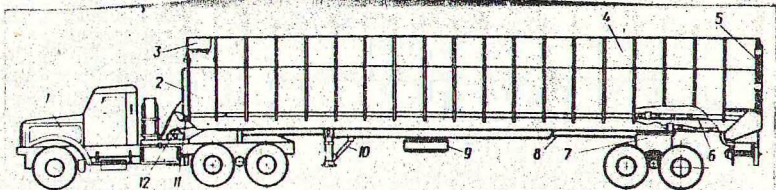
Щеповоз ЛТ-170: 1-автомобиль-тягач КраЗ-258Б1; 2-кузов; 3-тент; 4-борт надставной; 5-задний борт; 6-транспортер разгружающий; 7-тележка полуприцепа; 8-сцепка крестообразная; 9-колесо запасное полуприцепа; 10-устройство опорно-стояночное; 11-электрооборудование; 12-пневмооборудование.
